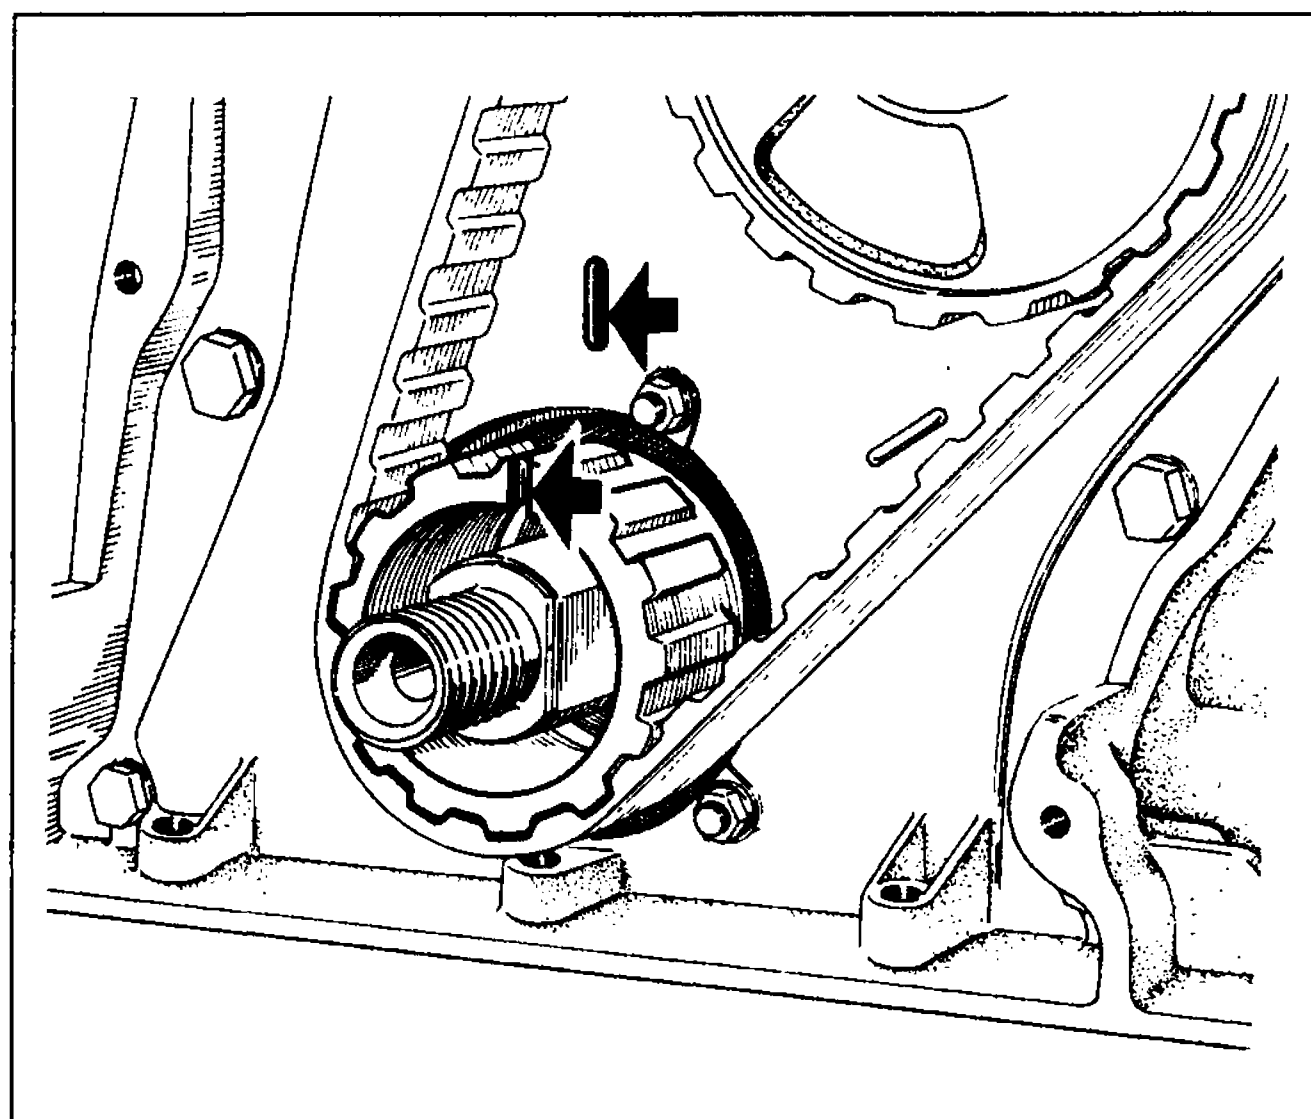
Проверка совпадения установочной метки на шкиве коленчатого вала с меткой на крышке привода распределительного вала
